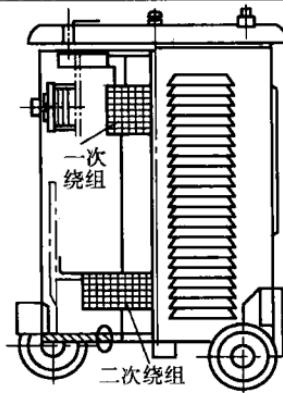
BX3—330 型弧焊变压器焊接电流的调节
